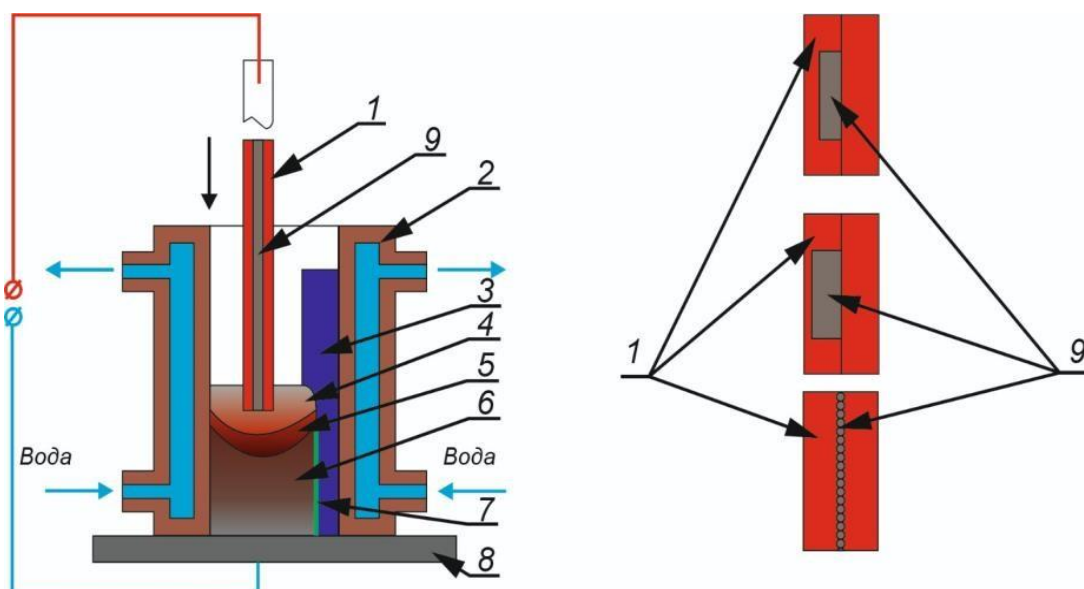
Схема процесу електрошлакового наплавлення пластинчастими електродами [70]: 1 – складовий пластинчастий електрод; 2 – водоохолоджуваний кристалізатор; 3 – виріб, що відновлюється; 4, 5 – шлакова та металева ванни; 6 – наплавлений метал; 7 – лінія сплавлення; 8 – піддон; 9 – шихтовий матеріал
